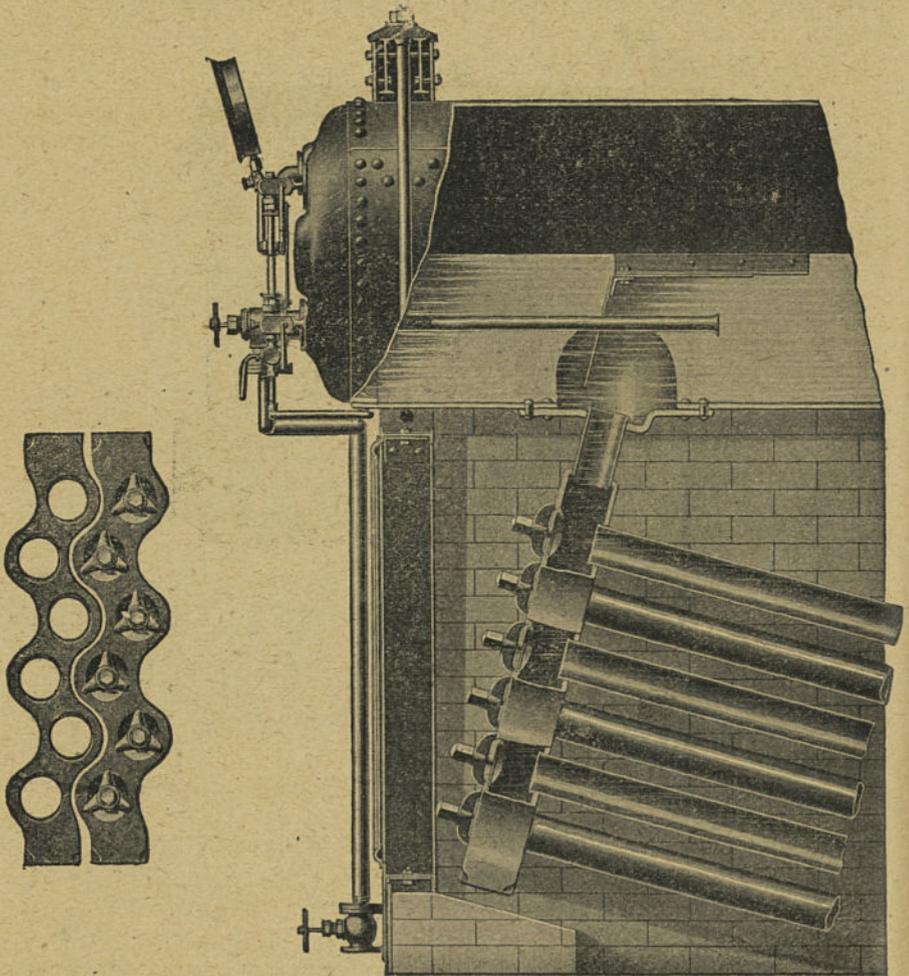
et 345. — Générateur à tubes d'eau Babcock et Wilcox (coupe).
